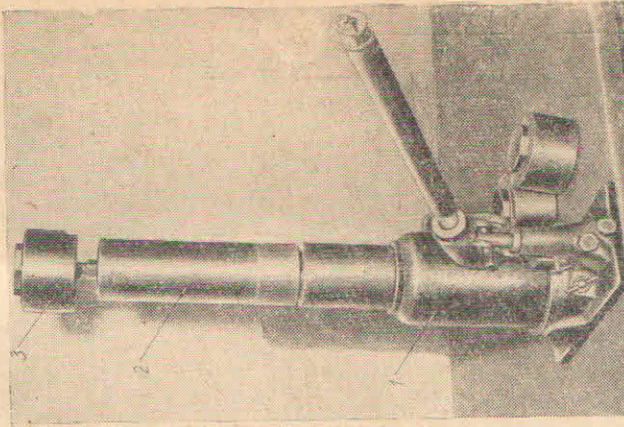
Приспособление для заполнения пресс-форм сырой резиной.
